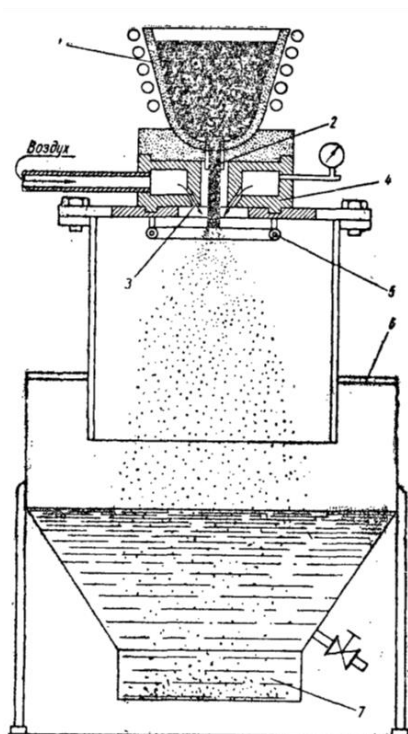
Схема метода получения порошков распылением жидкого металла водой и воздухом: 1 – тигель; 2 – отверстие; 3 – подача воздуха; 4 – кольцевая форсунка; 5 – видовой душ; 6 – кожух; 7 – бак с водой
